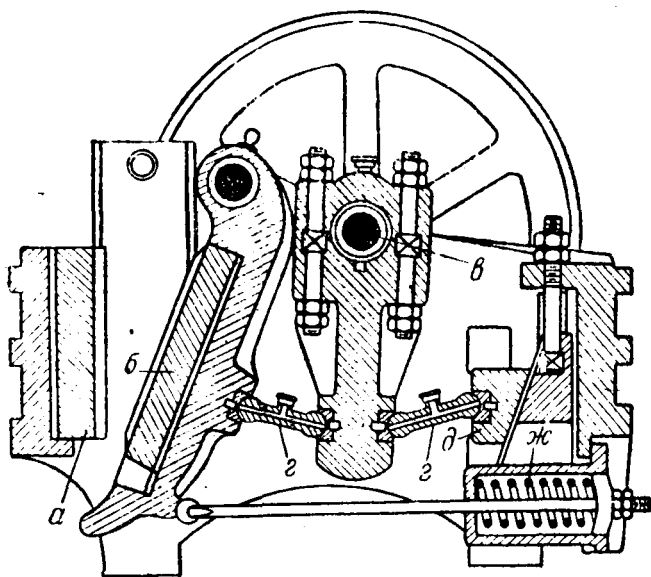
Дробилка „Блэк“. Разрез: а — неподвижная щека, б — подвижная щека, в — эксцентриковый вал, г — распорные плиты, д — клин, ж — пружина
